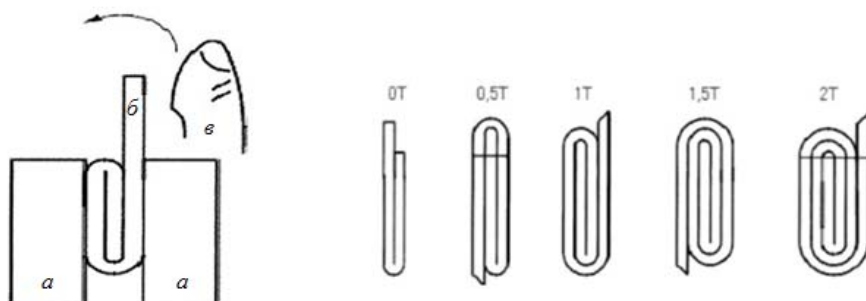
Испытание на изгиб: а – тиски; б – образец; в – палец
